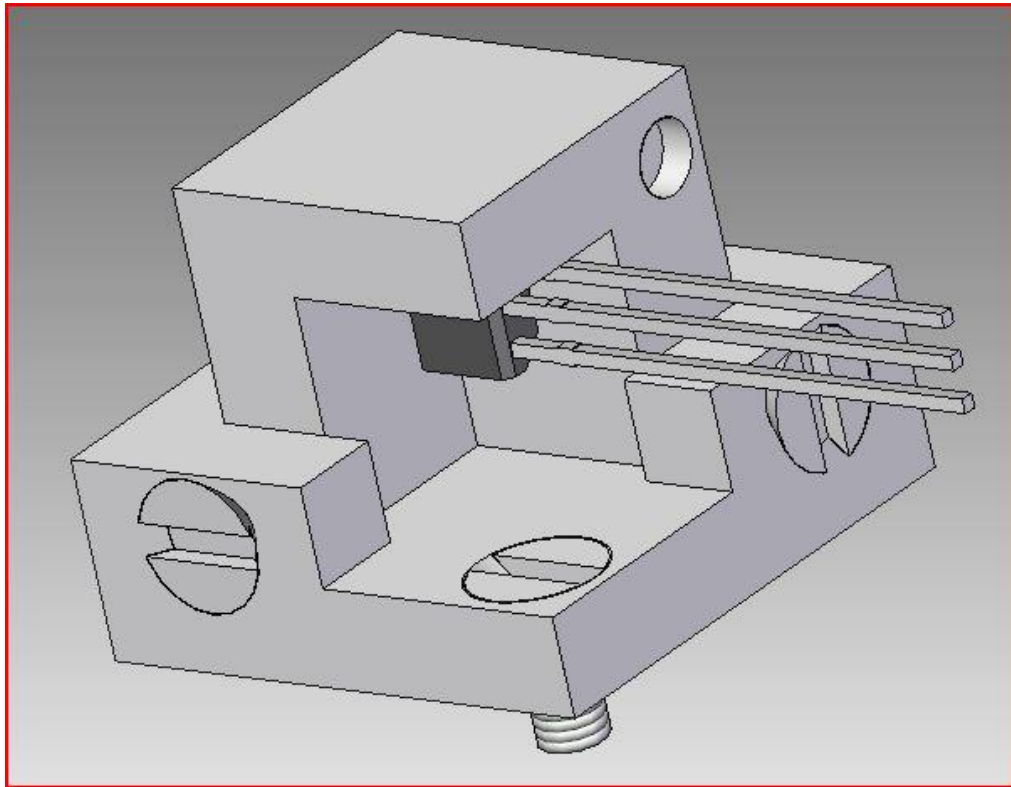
Diseño final en Solid Edge de cubo seccionado, posición 2
